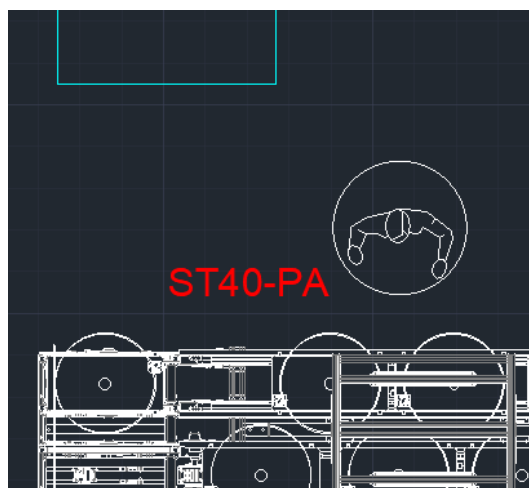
Puesto de montaje Estación ST40-PA. (Fuente: Elaboración propia)
